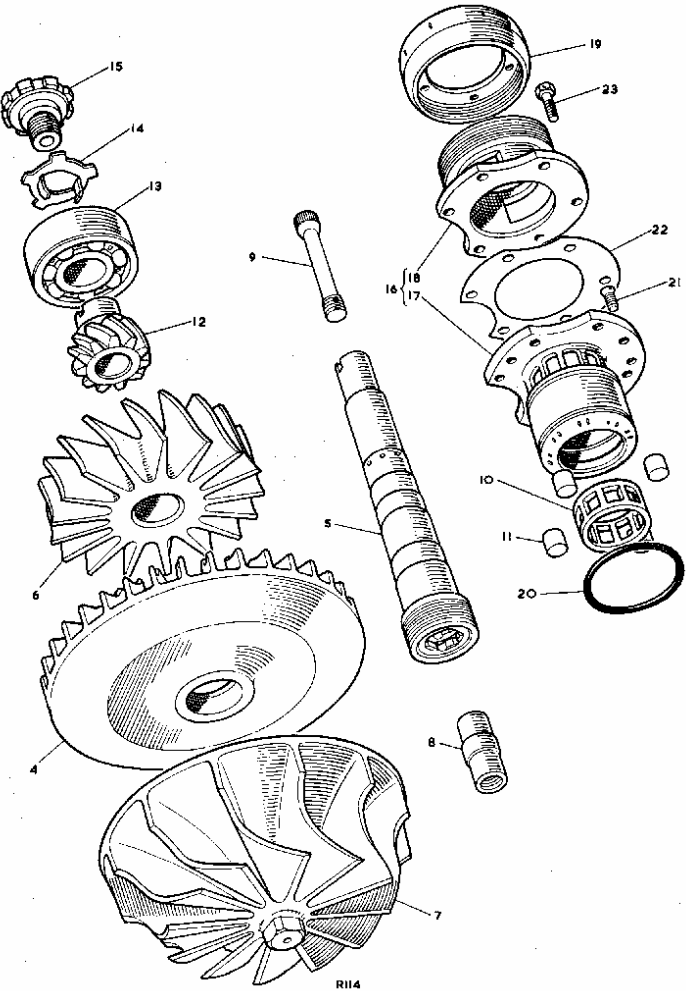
Explosionszeichnung des Gasgeneratorläufers [5]
